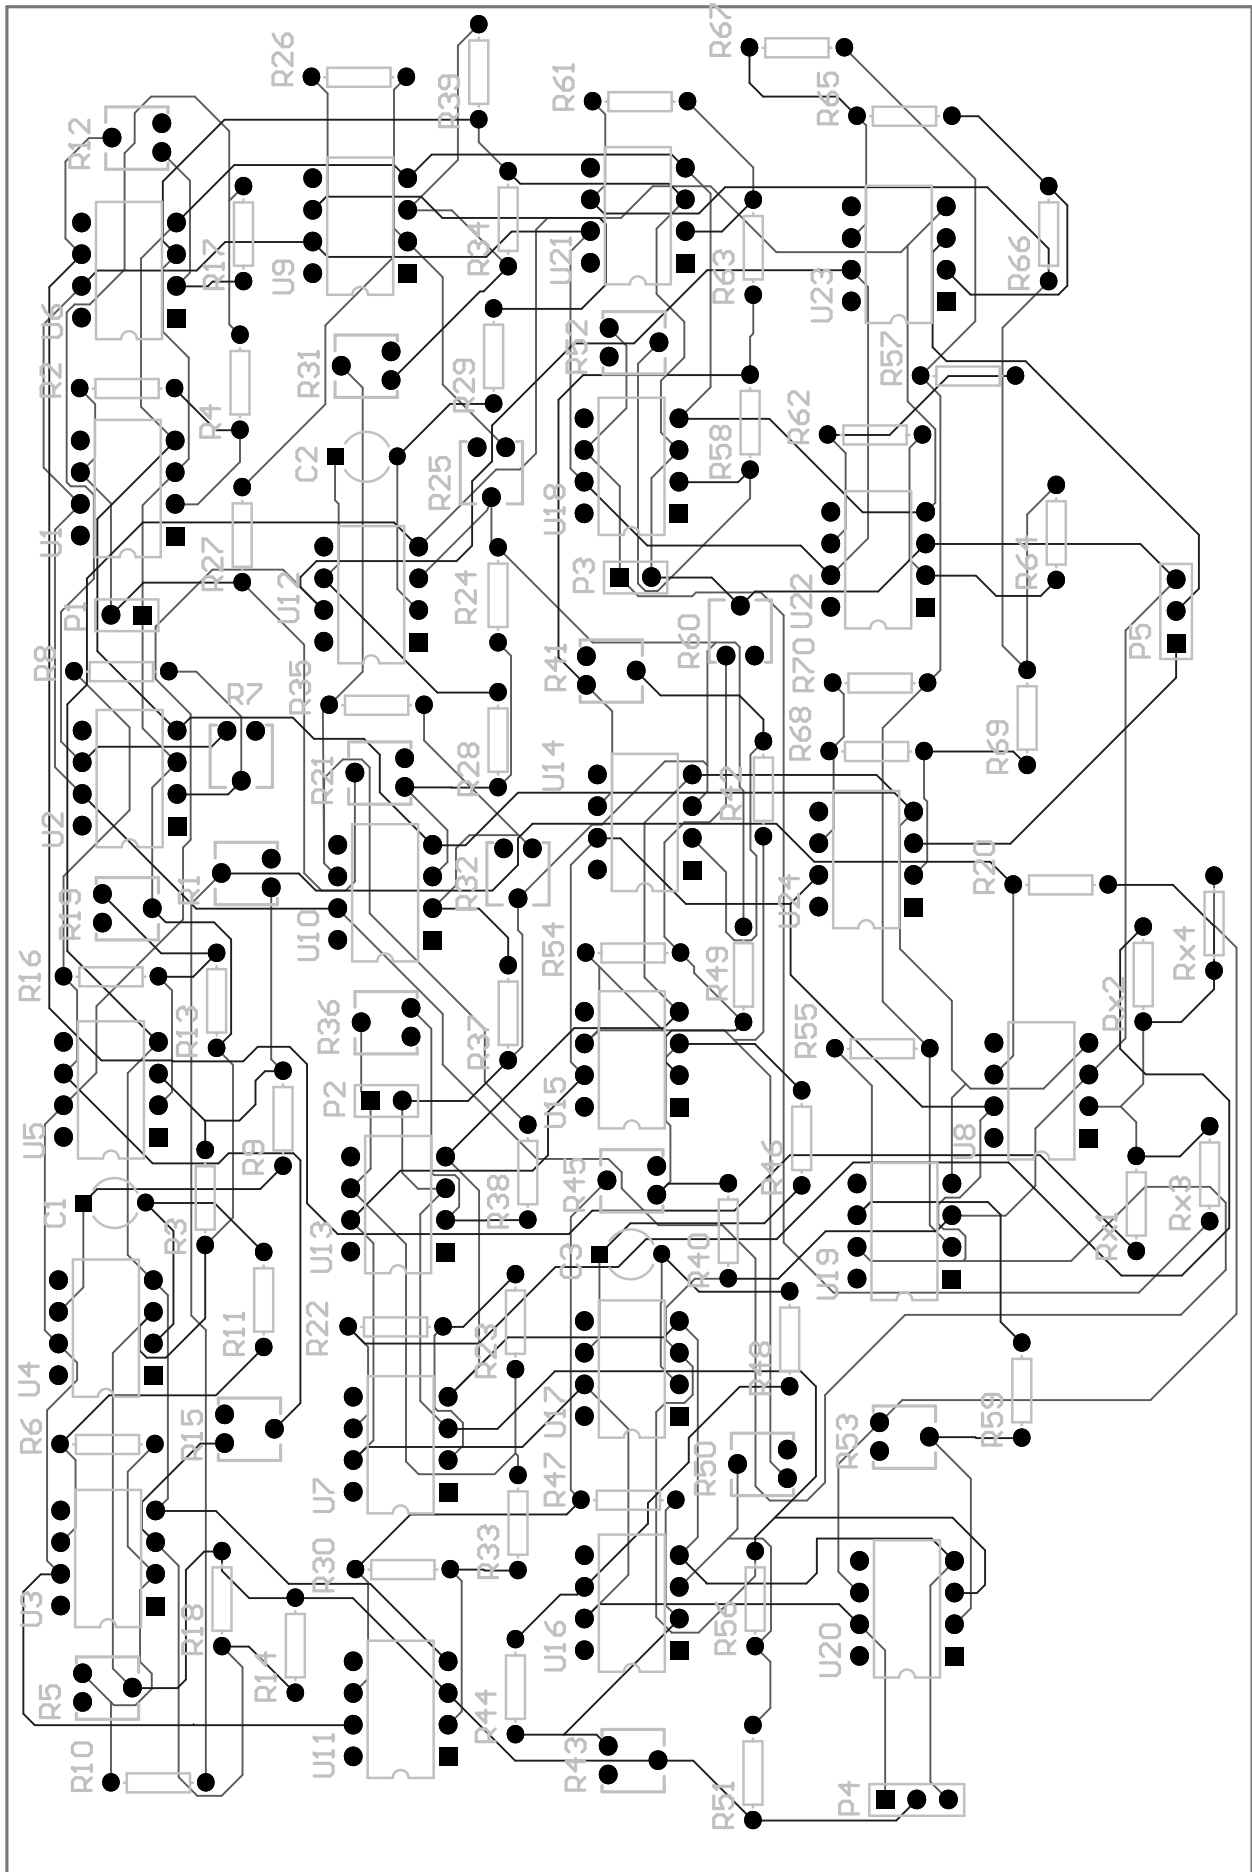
Diseño PCB para un oscilador caótico fraccionario de Lü con 4 enrollamientos.
